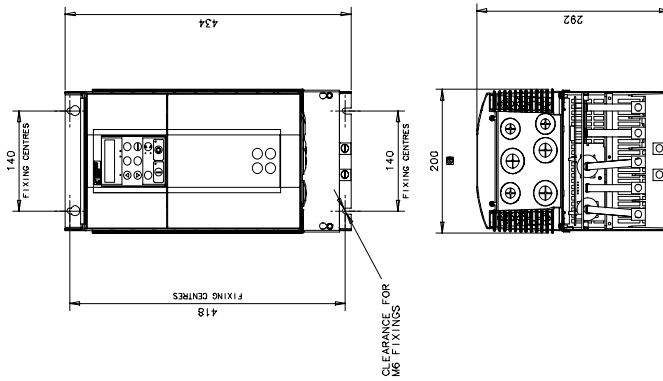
Taille 2 - Ensemble de puissance 40 - 165A
